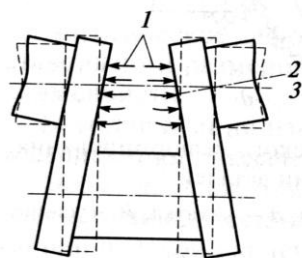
Схема правки коленчатого вала чеканкой:
